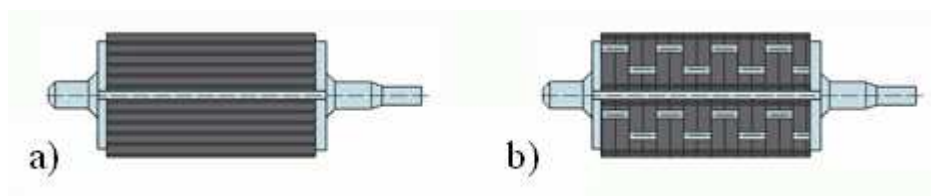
Keramické obložení bubnů Flex-Lag Weld [17]
